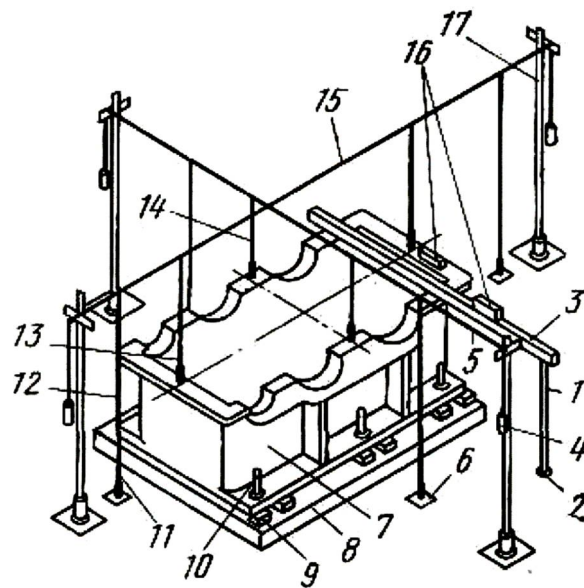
Вивірка рами рольганга струнним методом: 1 – штіх-масс; 2 – репер; 3 – повірочна лінійка; 4 – вантаж; 5 і 15 – струни; 6 – плашка; 7 – рама рольганга; 8 – фундамент; 9 – пакет підкладок; 10 – фундаментний болт; 11, 13 – схили; 12, 14 – нитки схилу; 16 – рівень; 17 – стойки
